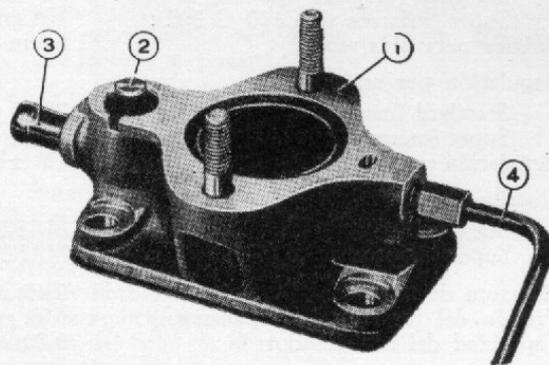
Cuerpo intermedio del carburador que sirve para la ventilación del cárter del cigüeñal.
